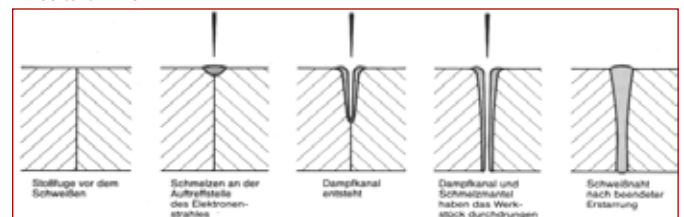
Prozessabfolge der Tiefenschweißung
